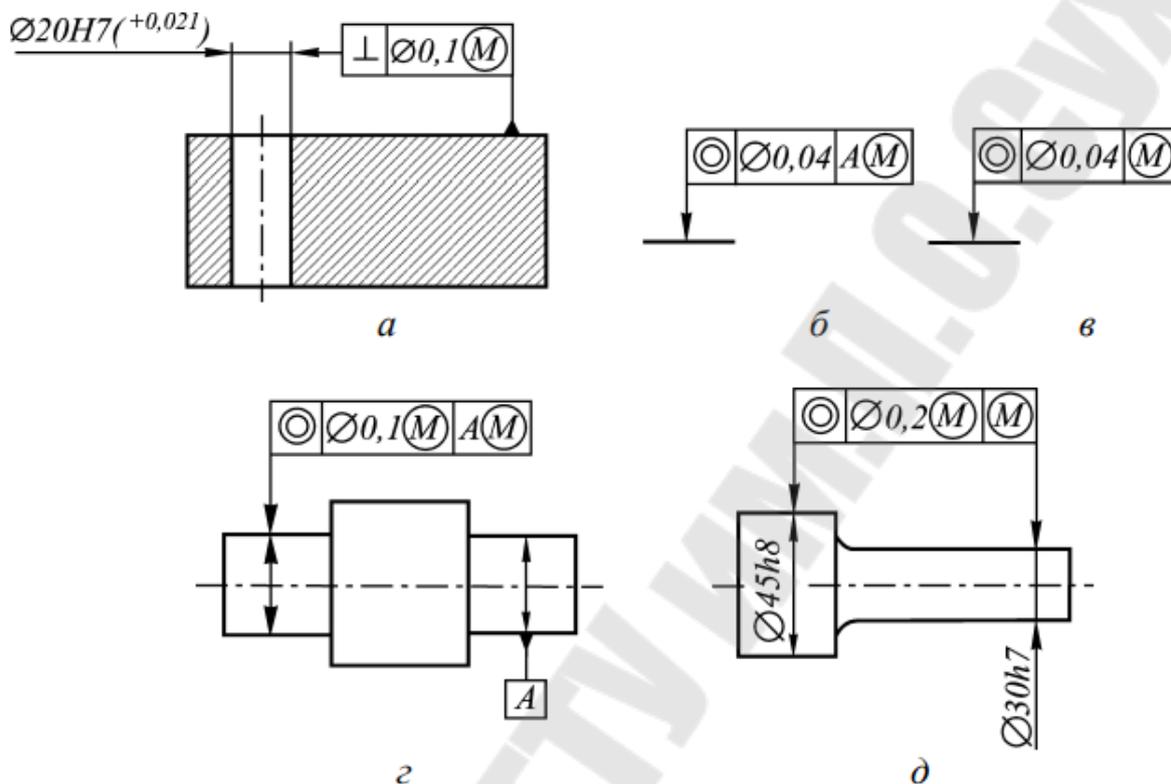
Обозначение на чертежах зависимых допусков формы и расположения поверхностей
